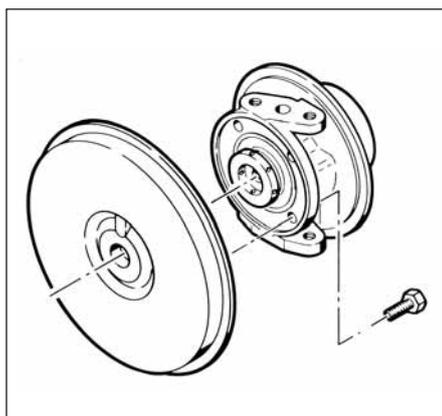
soltura do prato do compressor para modelos T04B, T04E, T31 e TE06
